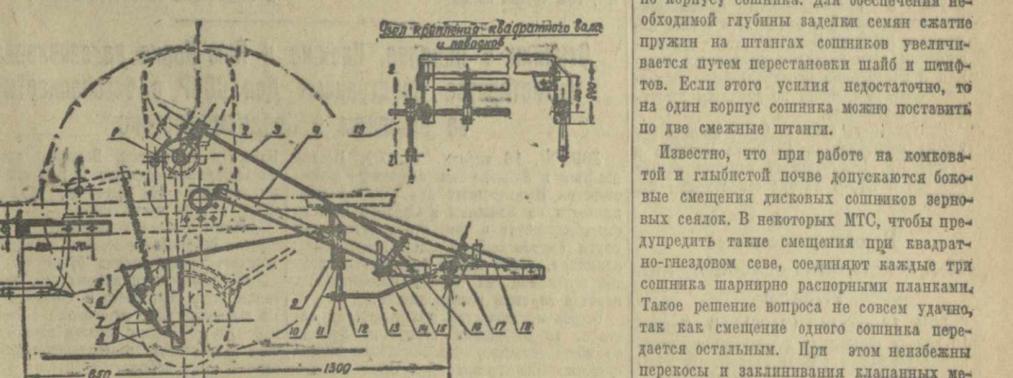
Переоборудованная зерновая селка для сева кукурузы (вид сбоку). 1—фиксатор; 2—храповой механизм; 3—тяга храпового механизма; 4 и 18—кронштейн узлоуловителя; 5—чистик; 6—тяга рычага клапана; 7—рычаг клапана; 8—копильник; 9—кронштейн квадратного вала; 10—квадратный вал; 11—сухарь; 12—гайка; 13—тяга узлоуловителя; 14—дополнительная вилка; 15—рычаг; 16—пружина рычага; 17—вилка узлоуловителя; 19—узел крепления квадратного вала и его поводков.
